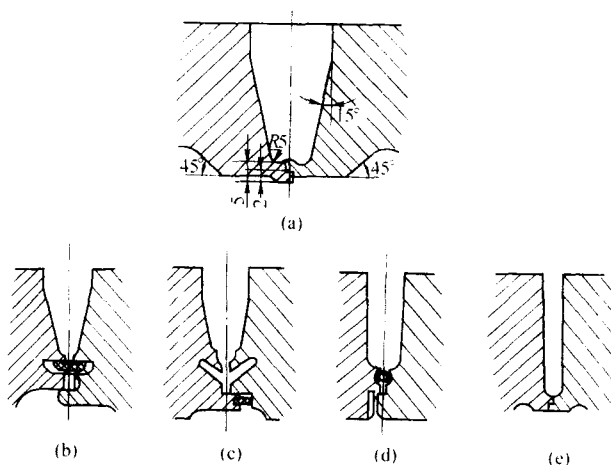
焊接转子焊接接头的结构形式
